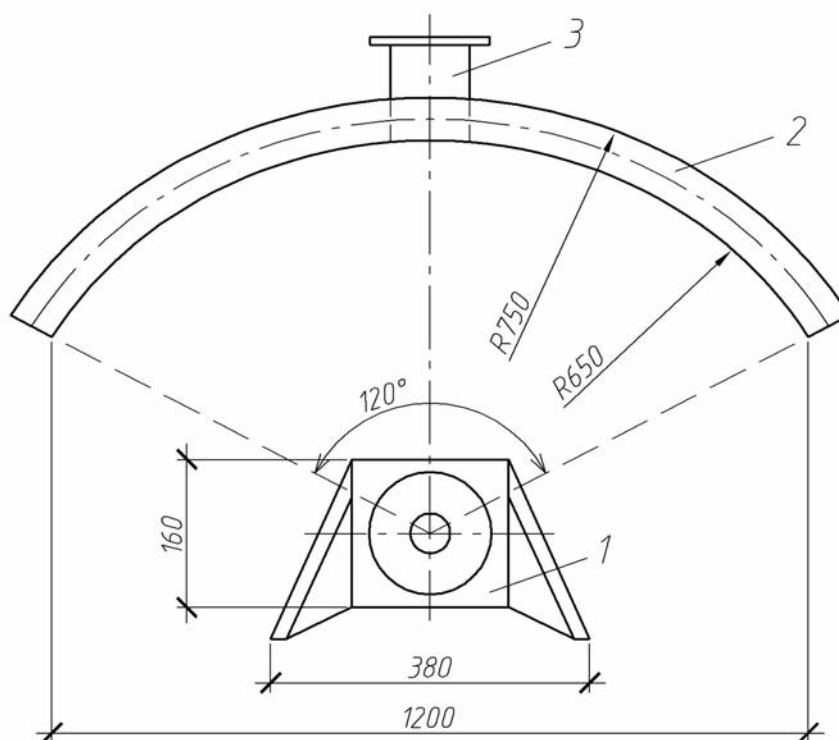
Схема усовершенствованного трубчатого инфракрасного нагревателя:
